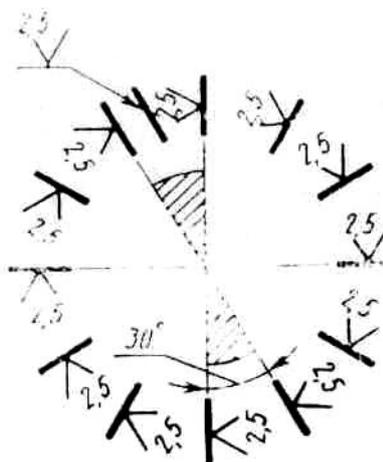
Обозначение шероховатости для всех поверхностей детали
